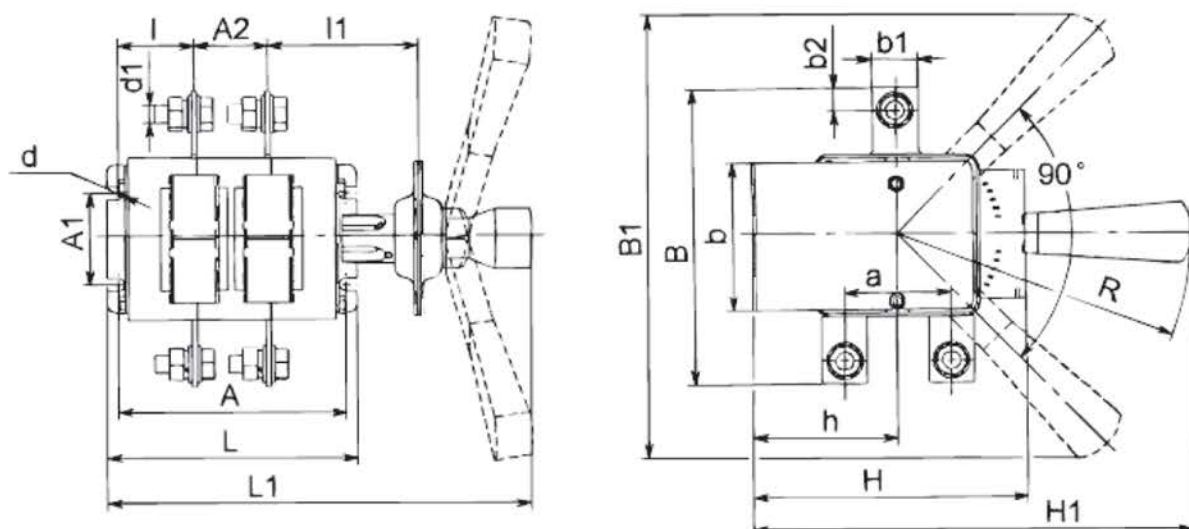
Выключатель-разъединитель двухполюсный на одно направление с передней смещенной рукояткой.
